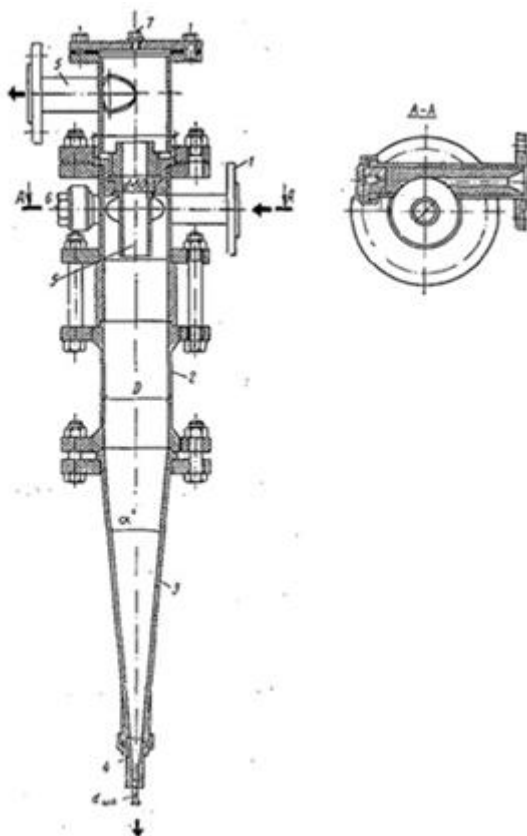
Конструкция напорного гидроциклона: 1 — питающий патрубок; 2 — цилиндрическая часть; 3 — коническая часть; 4 — шламовый патрубок; 5 — сливные патрубки; 6—ось подающей трубы; 7 — пробка для импульсной трубки
